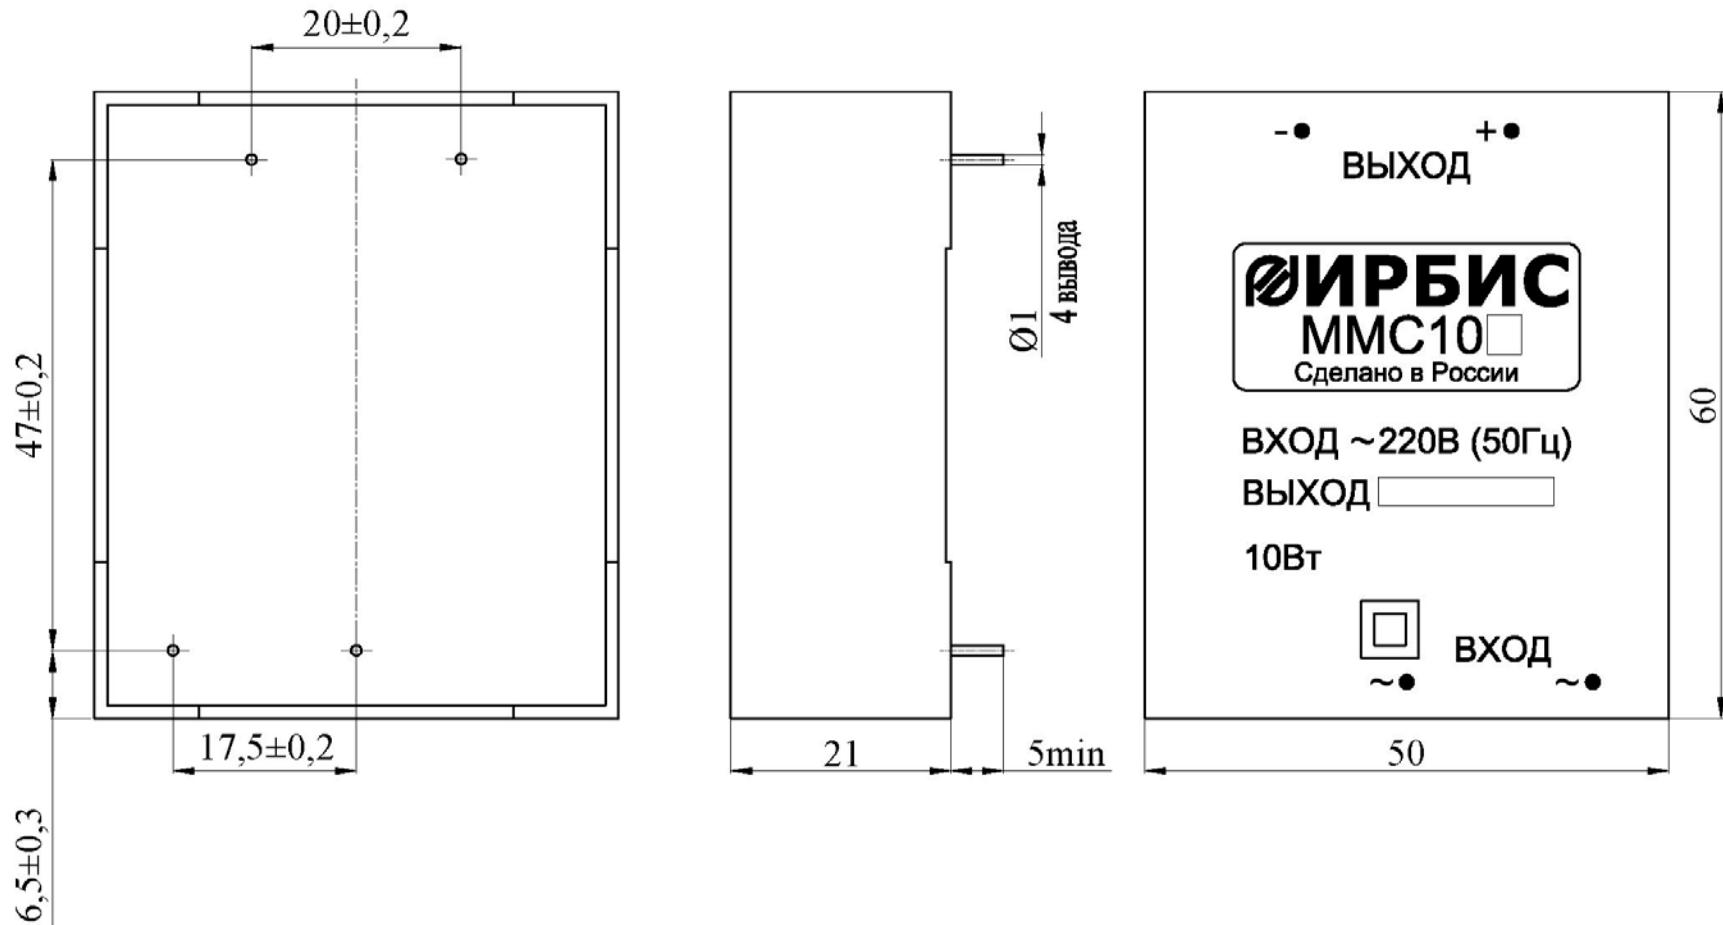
Габаритный чертеж модулей серии MMC10
